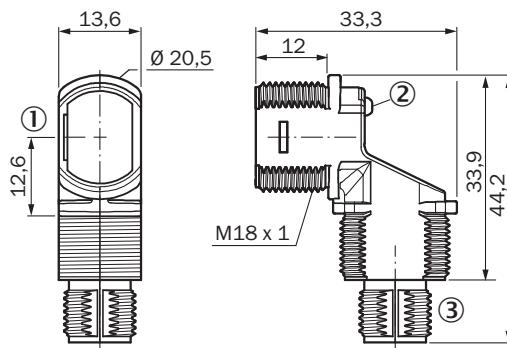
ZSE18-4xxxxx/ZSE18-Dxxxxx, M12-Steckverbinder
